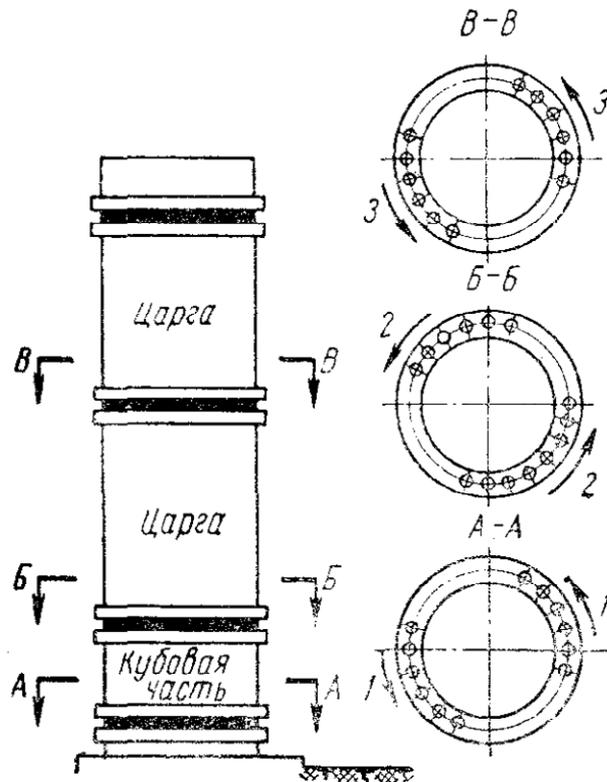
Схема порядка установки царг и затяжки фланцевых соединений:
